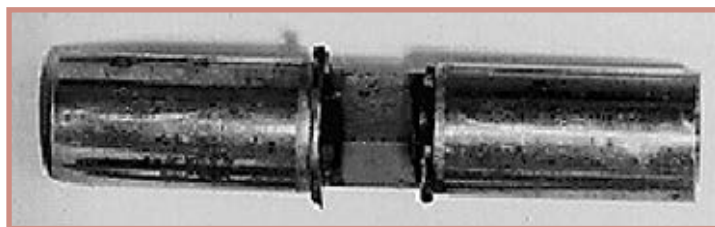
Заготовка образца Шарпи, реконструированная дуго-контактной сваркой
